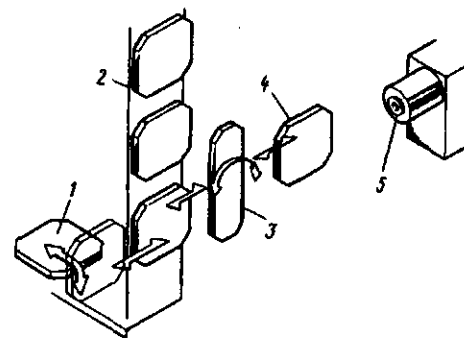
Схема автоматизированного загрузочного устройства – накопителя палет токарно-сверлильно-фрезерно-расточного станка: 1 – палета в позиции смены заготовки, детали; 2 – накопитель палет вертикального типа; 3 – манипулятор для смены палет; 4 – палета в рабочей позиции; 5 – шпиндель станка
